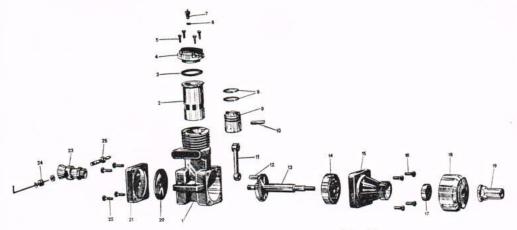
Vista esplosa di un motore a combustione interna Diesel.
